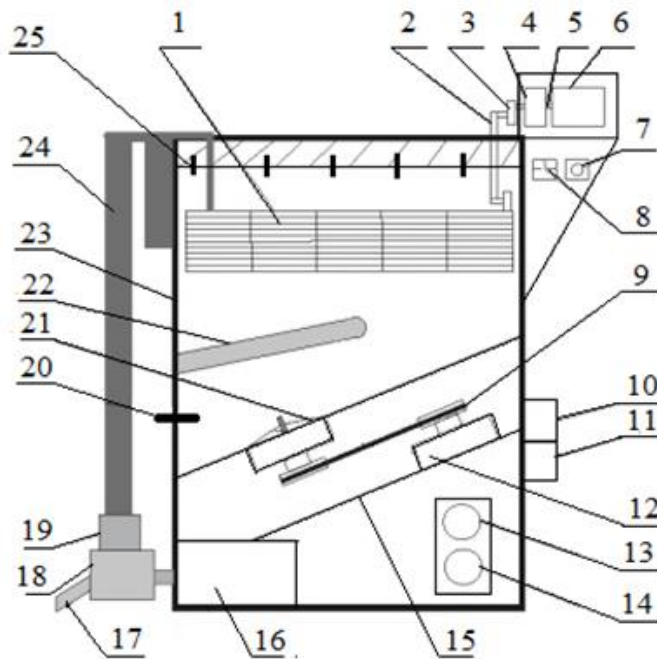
Схема оригинальной моечной установки для мойки деталей: 1 – корзина для размещения деталей (частота колебания 2 с^{-1}); 2 – шатун привода корзины; 3 – кривошип; 4 – редуктор ФШ-10/260Е; 5 – соединительная муфта; 6 – двигатель КФ 160-4/56Р (номинальная мощность 60 Вт); 7 – выключатель двигателя привода КШМ; 8 – выключатель двигателя привода жидкостного насоса; 9 – клиноременная передача привода центрифуги; 10 – автомат общего питания на 220 В; 11 – автомат выключения ТЭНа; 12 – реверсивный электродвигатель ДАО (номинальная мощность 160 Вт); 13 – таймер-выключатель двигателя привода центрифуги; 14 – реверс-выключатель привода центрифуги; 15 – наклонная рама; 16 – двигатель привода жидкостного насоса; 17 – сливной кран; 18 – жидкостный насос; 19 – фильтр очистки моющего раствора; 20 – термометр; 21 – дисковый активатор моющего раствора (центрифуга); 22 – электроиндукционный нагреватель (ТЭН мощностью 2,0 кВт); 23 – емкость установки (30 л); 24 – система подачи жидкости под давлением; 25 – форсунки
